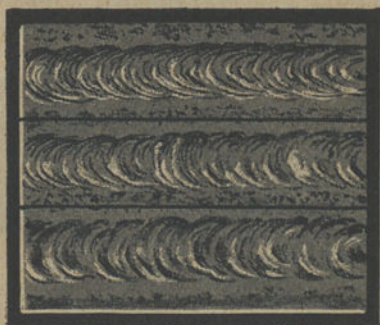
Soldaduras em chapas de 2 mm.
